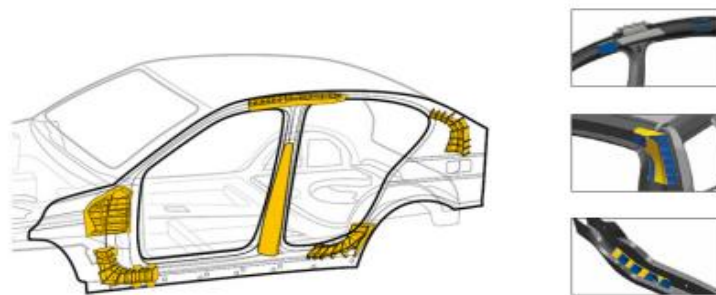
Locais de aplicação da tecnologia de reforço estrutural [5]
